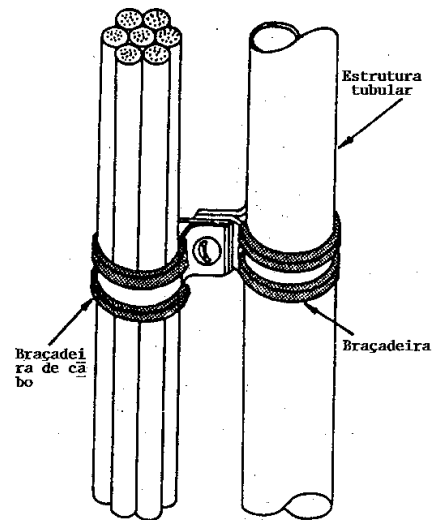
Instalação da braçadeira de cabo na estrutura tubular.
